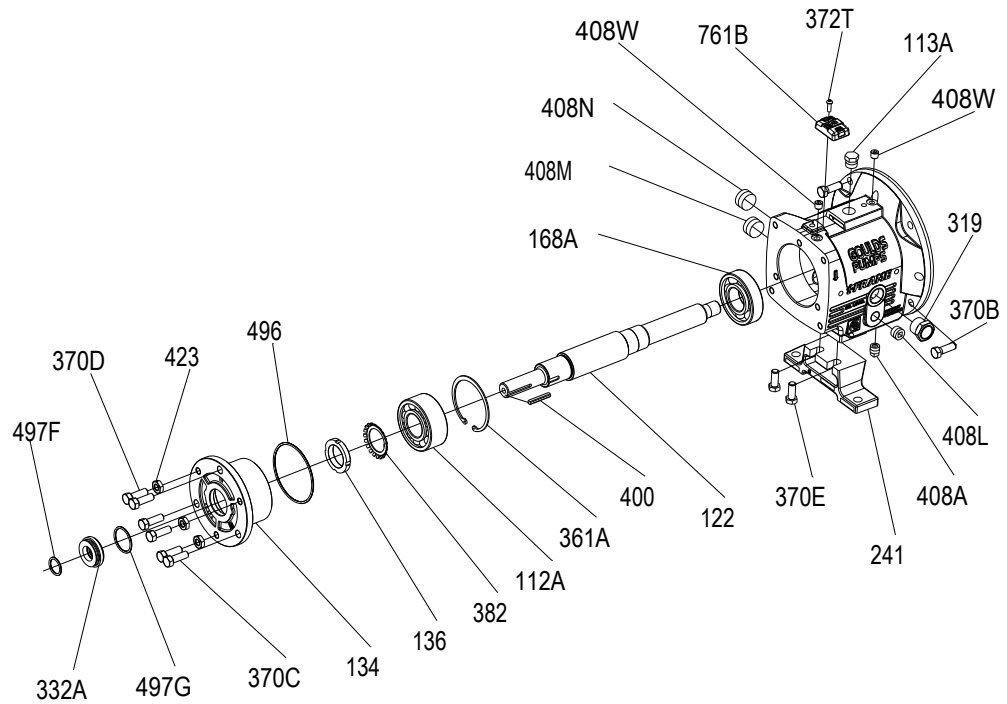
MTi-Stützschaale Explosionszeichnung
